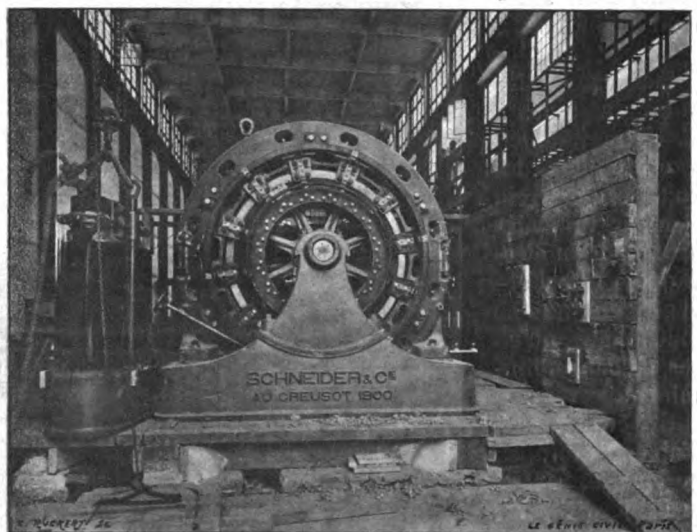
Vue d'un alternateur, prise pendant son montage, le 13 juillet 1900.
